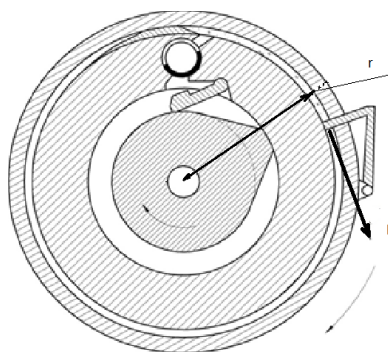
Кинематическая схема роторного двигателя конструкции АлтГТУ
